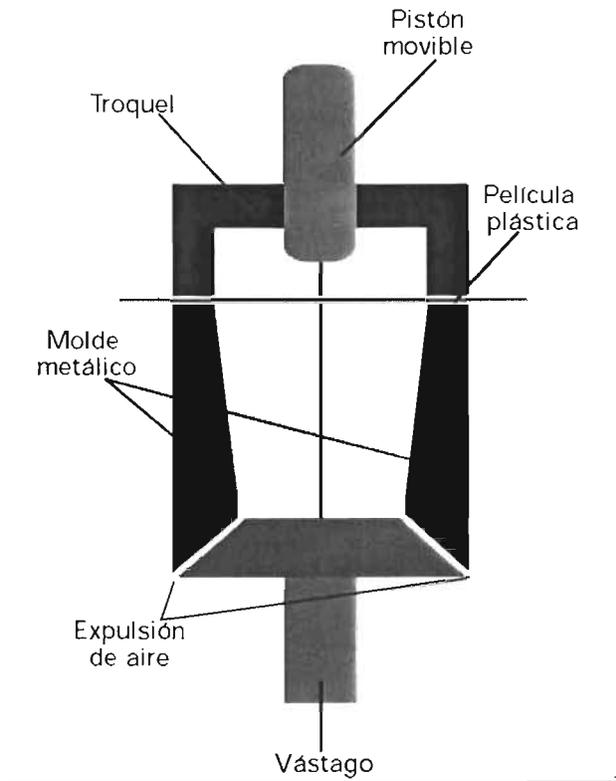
Partes de un molde para elaborar piezas profundas por termoformado
